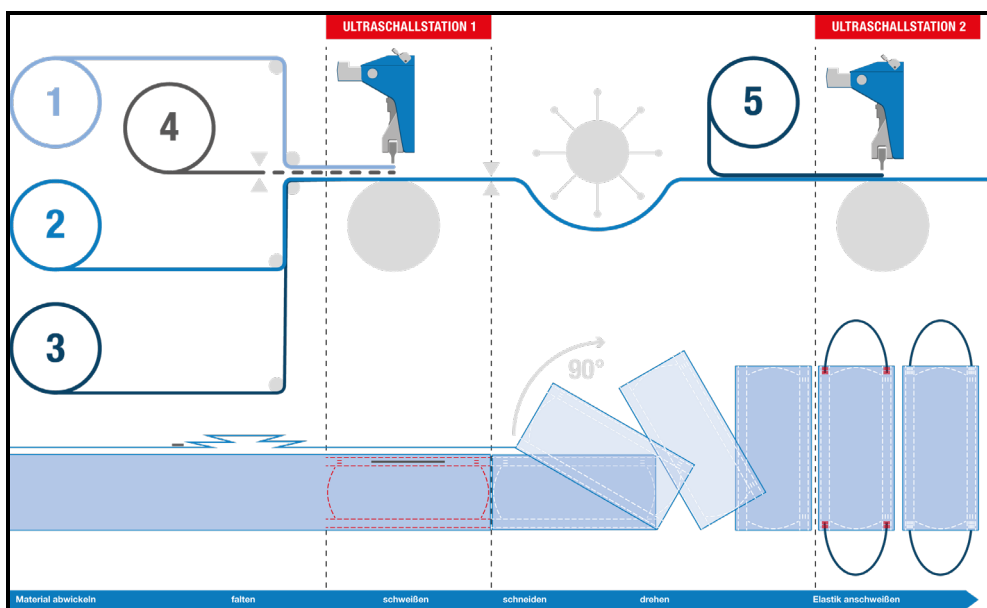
Funktionsprinzip einer vollautomatischen Maskenmaschine für flache OP-Masken
